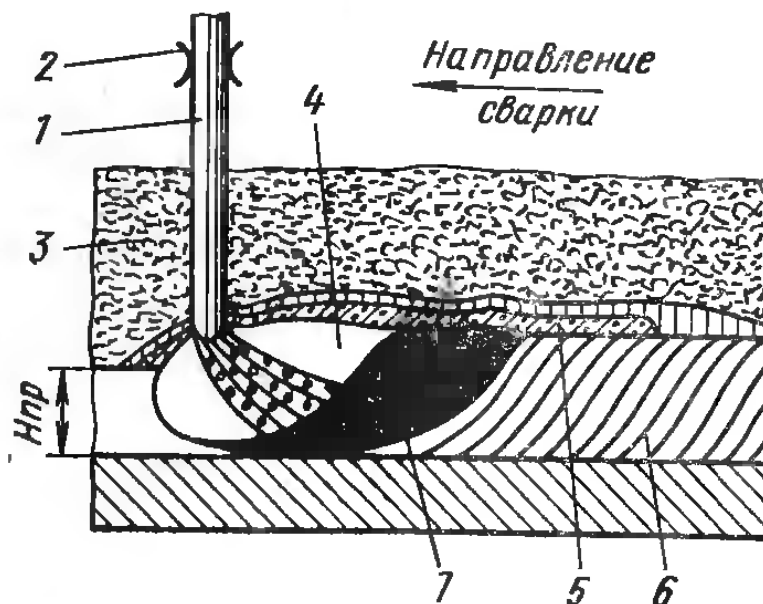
Схема процесса сварки под слоем флюса [1]
